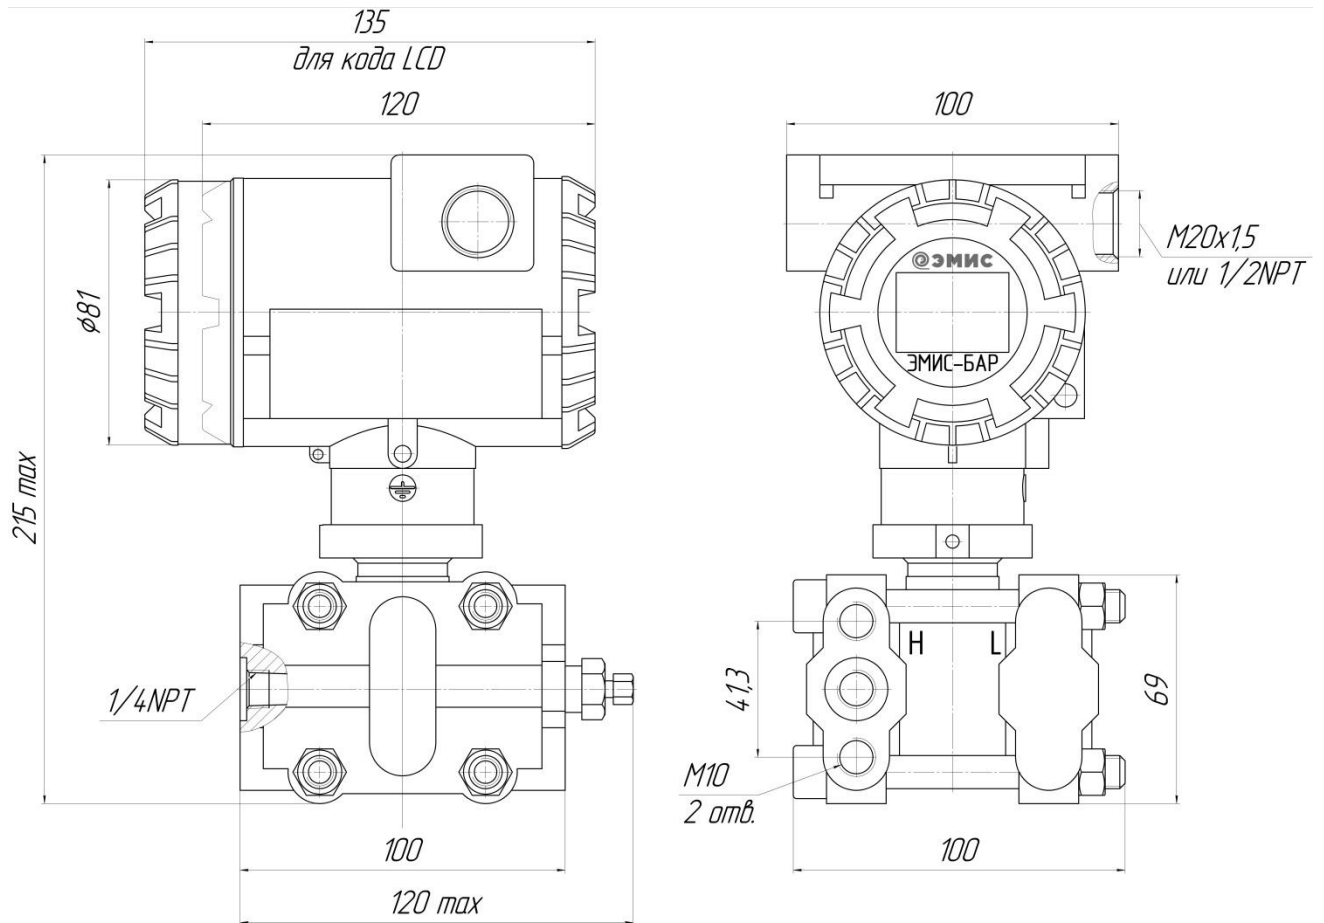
Габаритные и присоединительные размеры штуцерного исполнения датчиков давления ЭМИС-БАР 103 и 123
